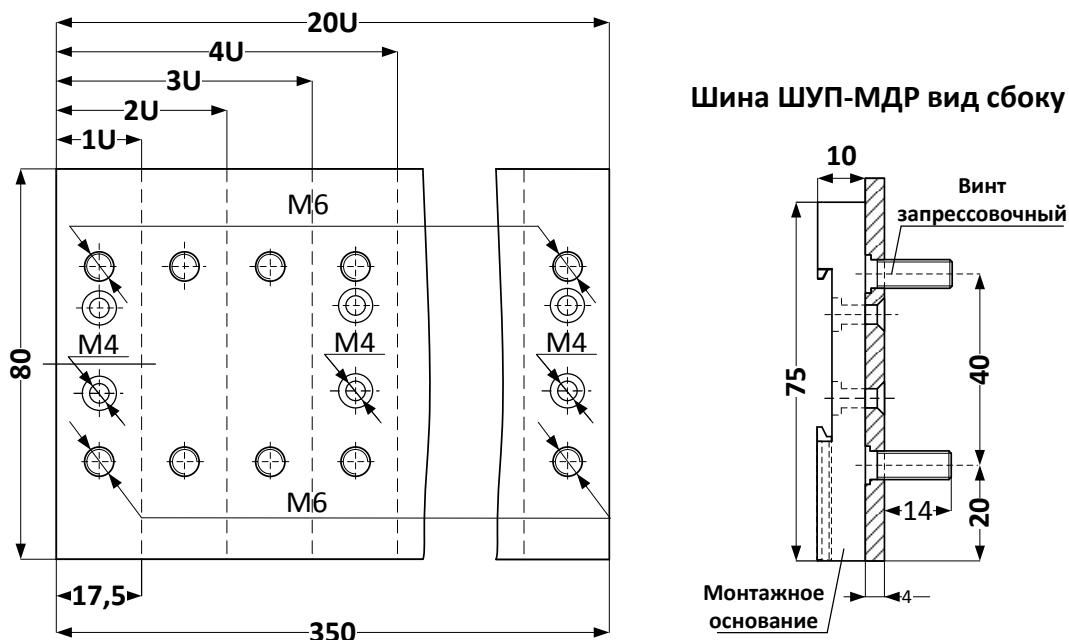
Конструкция и габаритные размеры шины ШУП-МДР.
